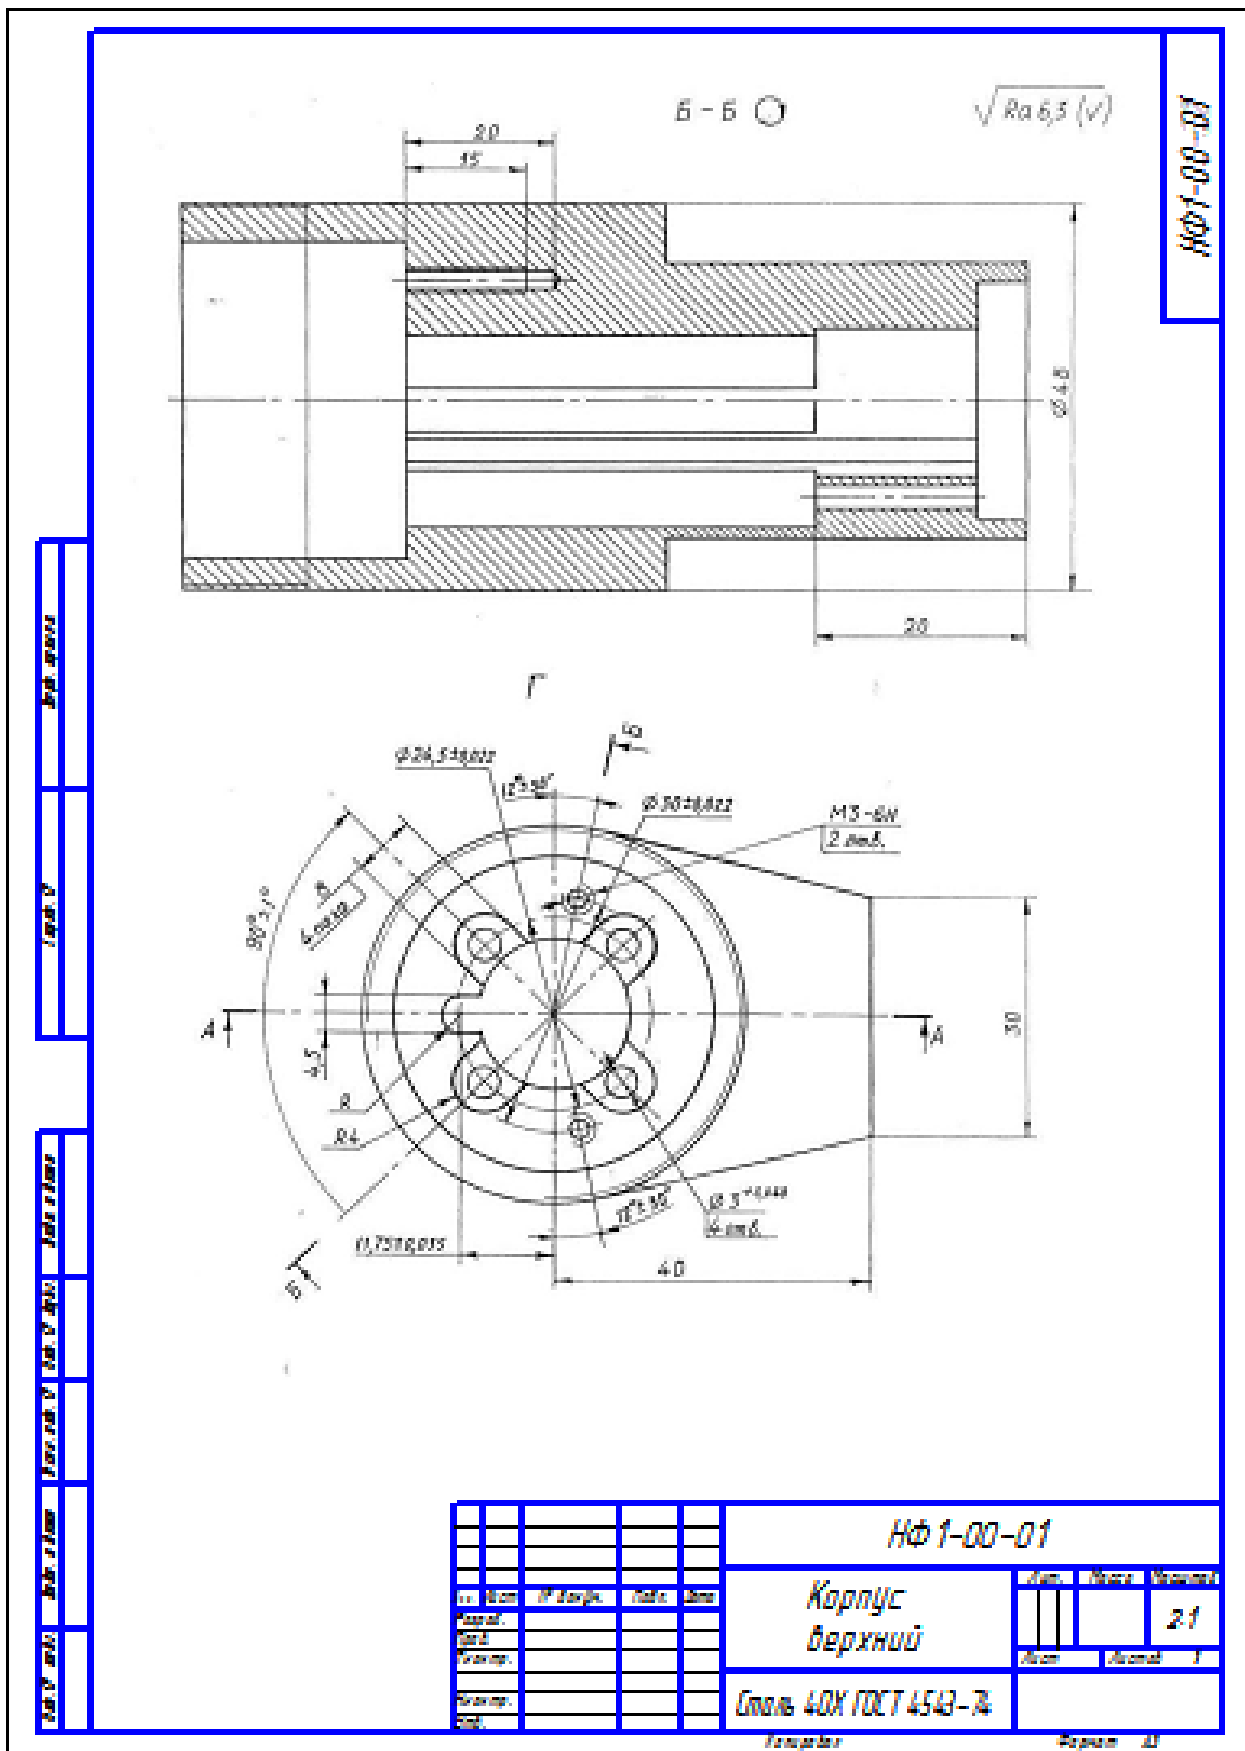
а. Пример выполнения рабочего чертежа детали «Корпус верхний»
